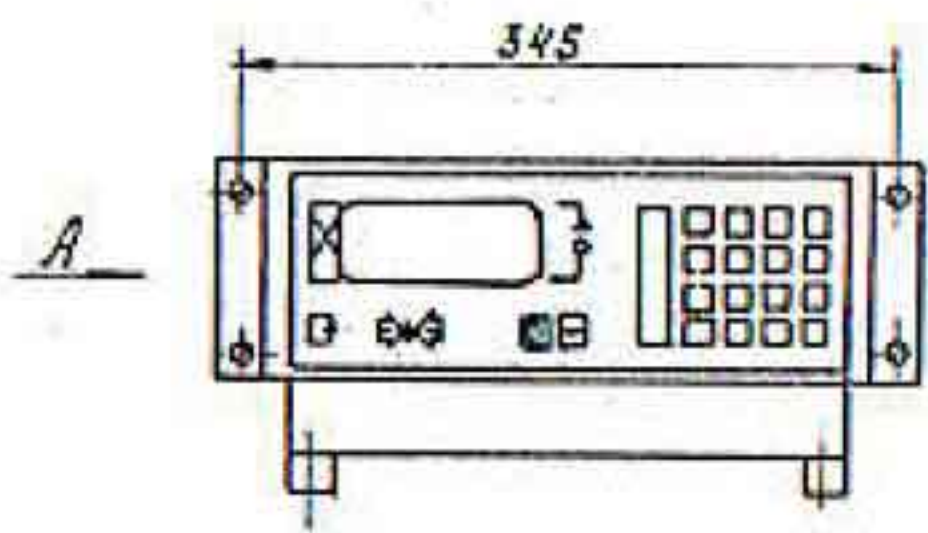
Габаритный чертеж и установочные размеры УЦЦ
